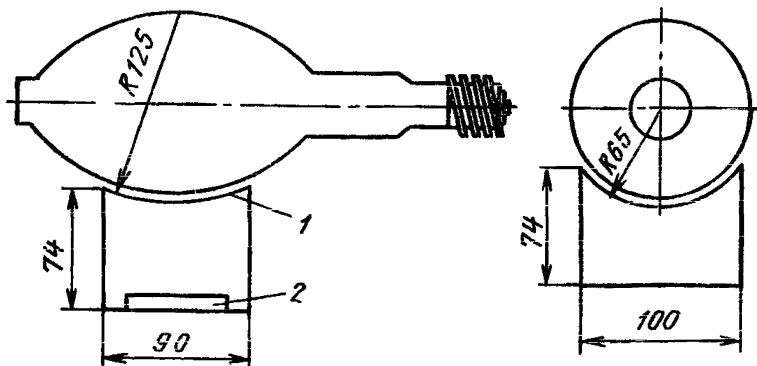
Приставка для измерения светового потока ламп типа ДРЛ
